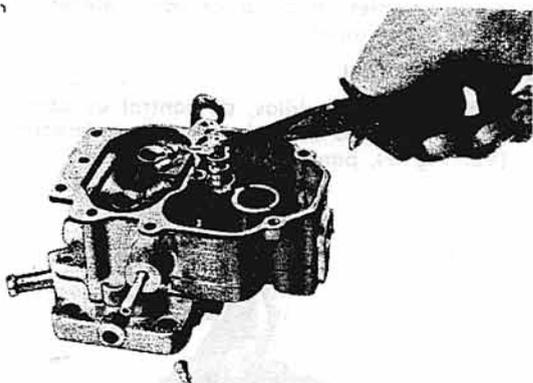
Desmontaje y montaje del pistón de sobre alimentación.
